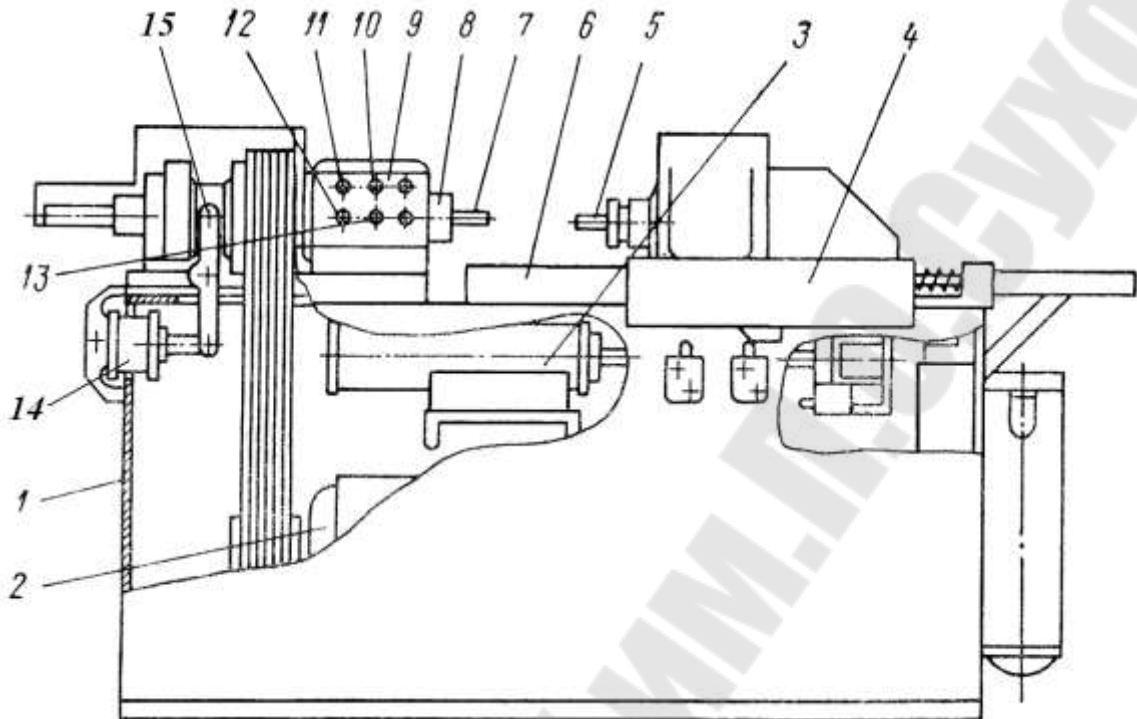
Эскиз общего вида специального сварочного полуавтомата модели МФ-327: 1 – станина; 2 – электродвигатель привода вращения шпинделя; 3 – пневмоцилиндр перемещения суппорта; 4 – суппорт; 5, 7 – свариваемые заготовки; 6 – направляющие суппорта; 8 – шпиндель; 9 – передняя бабка; 10 – кнопка «Пуск» суппорта; 11 – кнопка «Пуск» двигателя; 12 – кнопка «Стоп» двигателя; 13 – кнопка «Стоп» суппорта; 14 – пневмоцилиндр; 15 – рычаг переключения муфты
